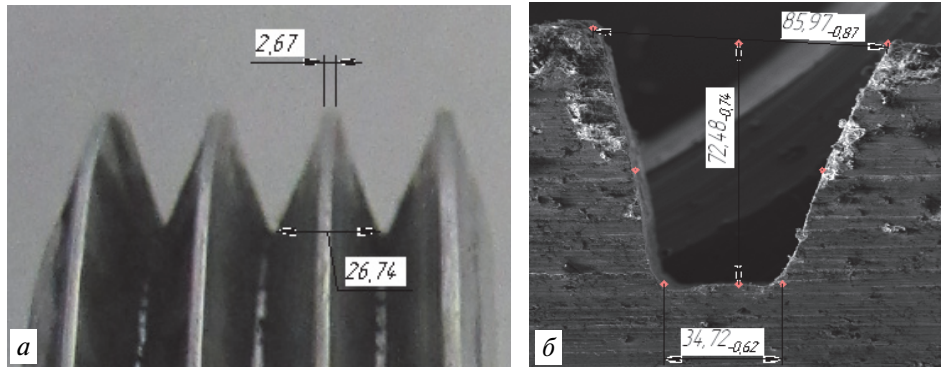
Профили образцов с размерами: *a* — образец — диск; *b* — образец — пластина
